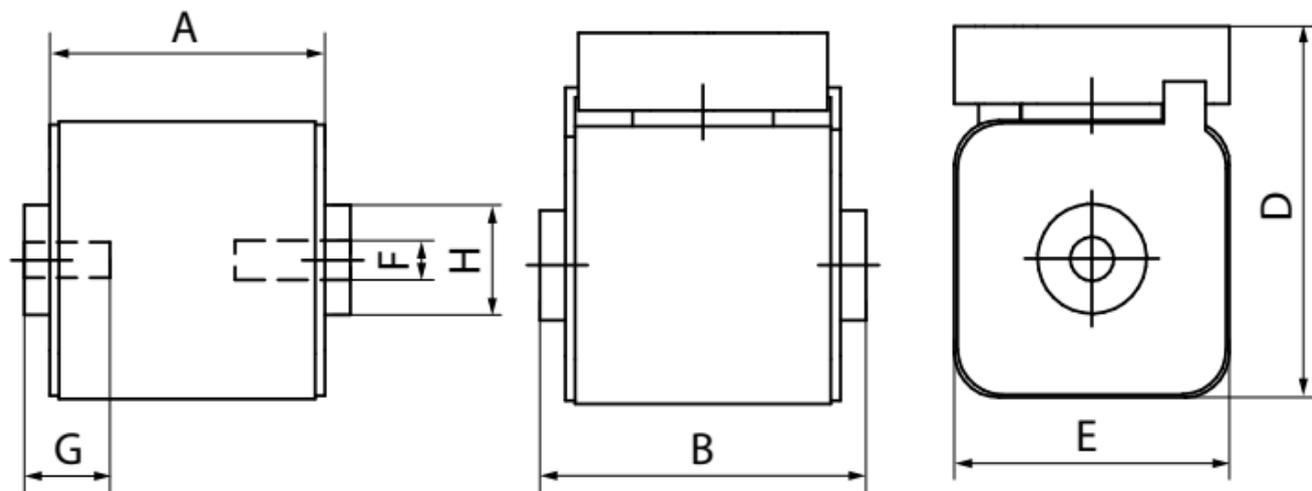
Размеры для габаритов S30, S31, S32, S33
